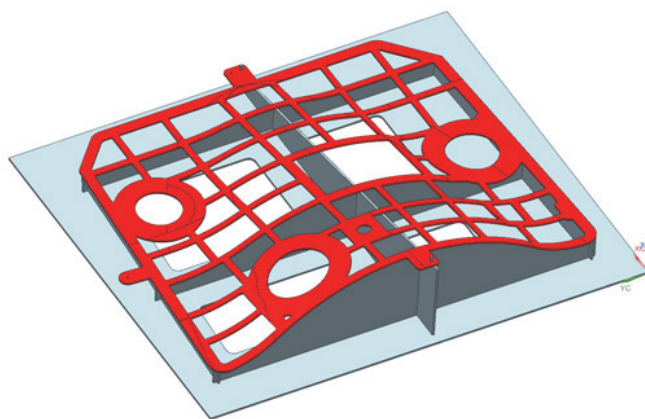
Деталь «Решетка» расположенная на приспособлении для гидроабразивной резки
